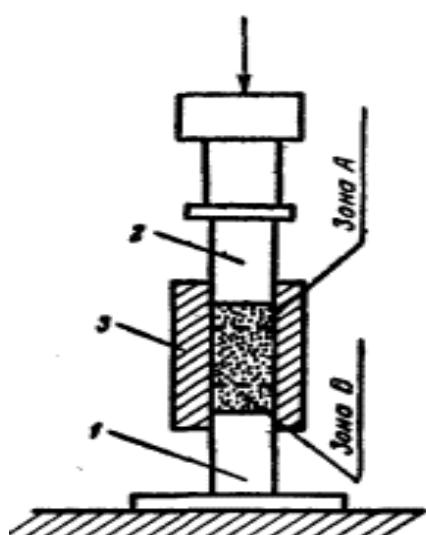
Схема двухстороннего прессования с плавающей формой.
